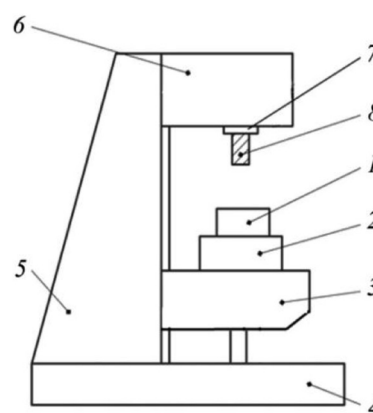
Компановка ТС: 1 – заготовка; 2 – приспособление; 3 – консольный стол; 4 – основание; 5 – стойка; 6 – шпиндельная бабка; 7 – шпиндель; 8 – инструмент
